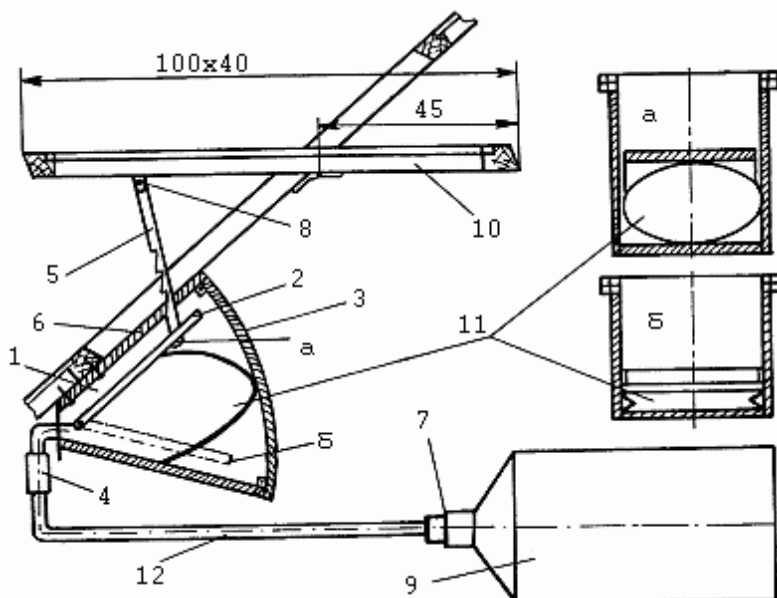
Устройство для автоматического регулирования температуры в парнике: 1 – корпус; 2 – клапан; 3 – смотровая крышка; 4 – соединительная муфта; 5 – толкатель; 6 – опорная пластина фрамуги; 7 – патрубок бачка; 8 – шарнир; 9 – расширительный бак; 10 – фрамуга; 11 – камера привода автомата; 12 – трубопровод; а – фрамуга открыта; б – фрамуга закрыта (размеры даны в см)
